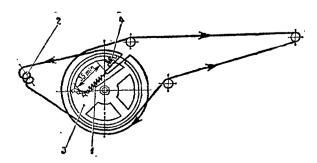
Книематическая схема верньерного устройства: 1 — шкив; 2 — ось ручки настройки; 3 — пружина; 4 — шайба
